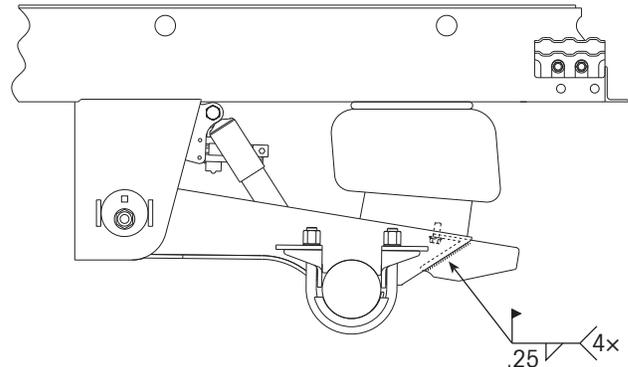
Detalles de soldadura de la extensión de la viga trasera (solamente kits SURELOK SLKM y SLKR)
